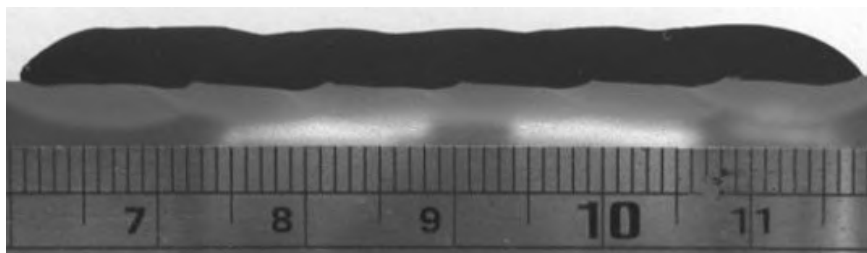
Seção transversal de revestimento soldado (SILVA, 2010).
